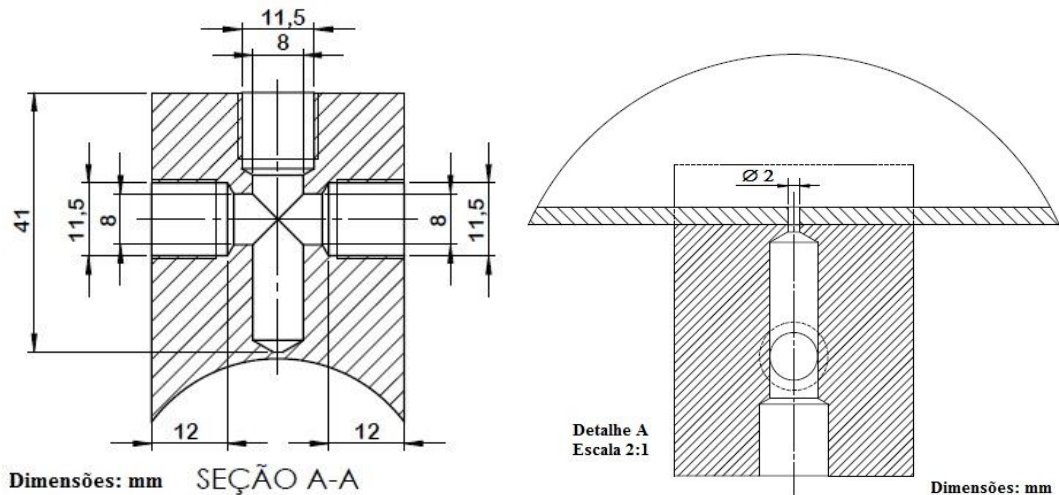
Desenhos de projeto do injetor mostrando suas principais dimensões
